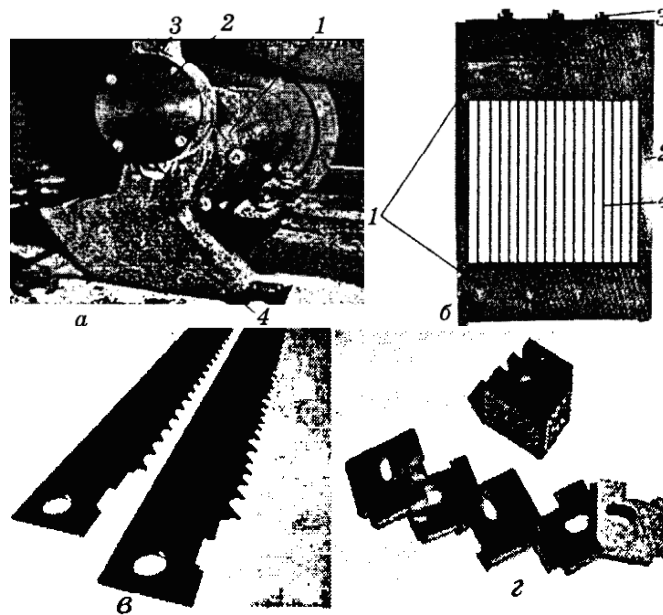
Елементи механізму різання міні-рами: а – кривошипно-повзунний механізм: 1 – вал на підшипникових опорах; 2 – підшипниковий вузол; 3 – шатун; 4 – кривошип; б – пилкова рамка: 1 – поперечини; 2 – вертикальні стійки; 3 – гвинтовий механізм натягування пилок; 4 – постав пилок; в – пилки; г – міжпилкові прокладки
